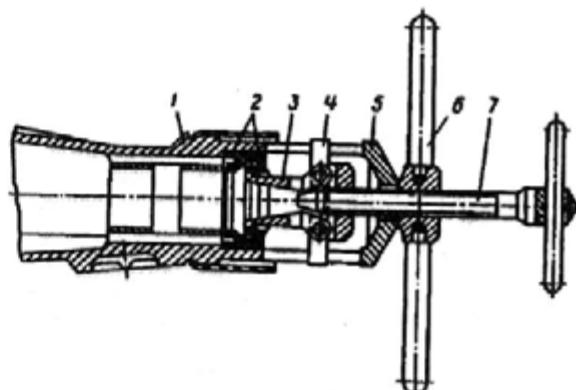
Выпрессовка сальника из горловины удлинителя с помощью съемника:
